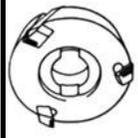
Auch alte Maschinen arbeiten wieder wirtschaftlich, wenn ein leicht schneidender Fräser benutzt wird.
